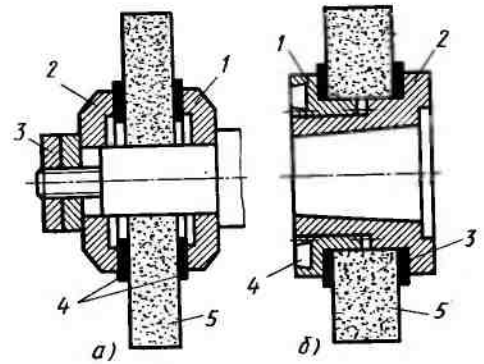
Схемы крепления шлифовальных кругов: а — фланцами; 1, 2 — фланцы, 3 — гайки, 4 — прокладки, 5 — круг; б — на переходных фланцах; 4 — кольцевой паз, 3 — прокладка
